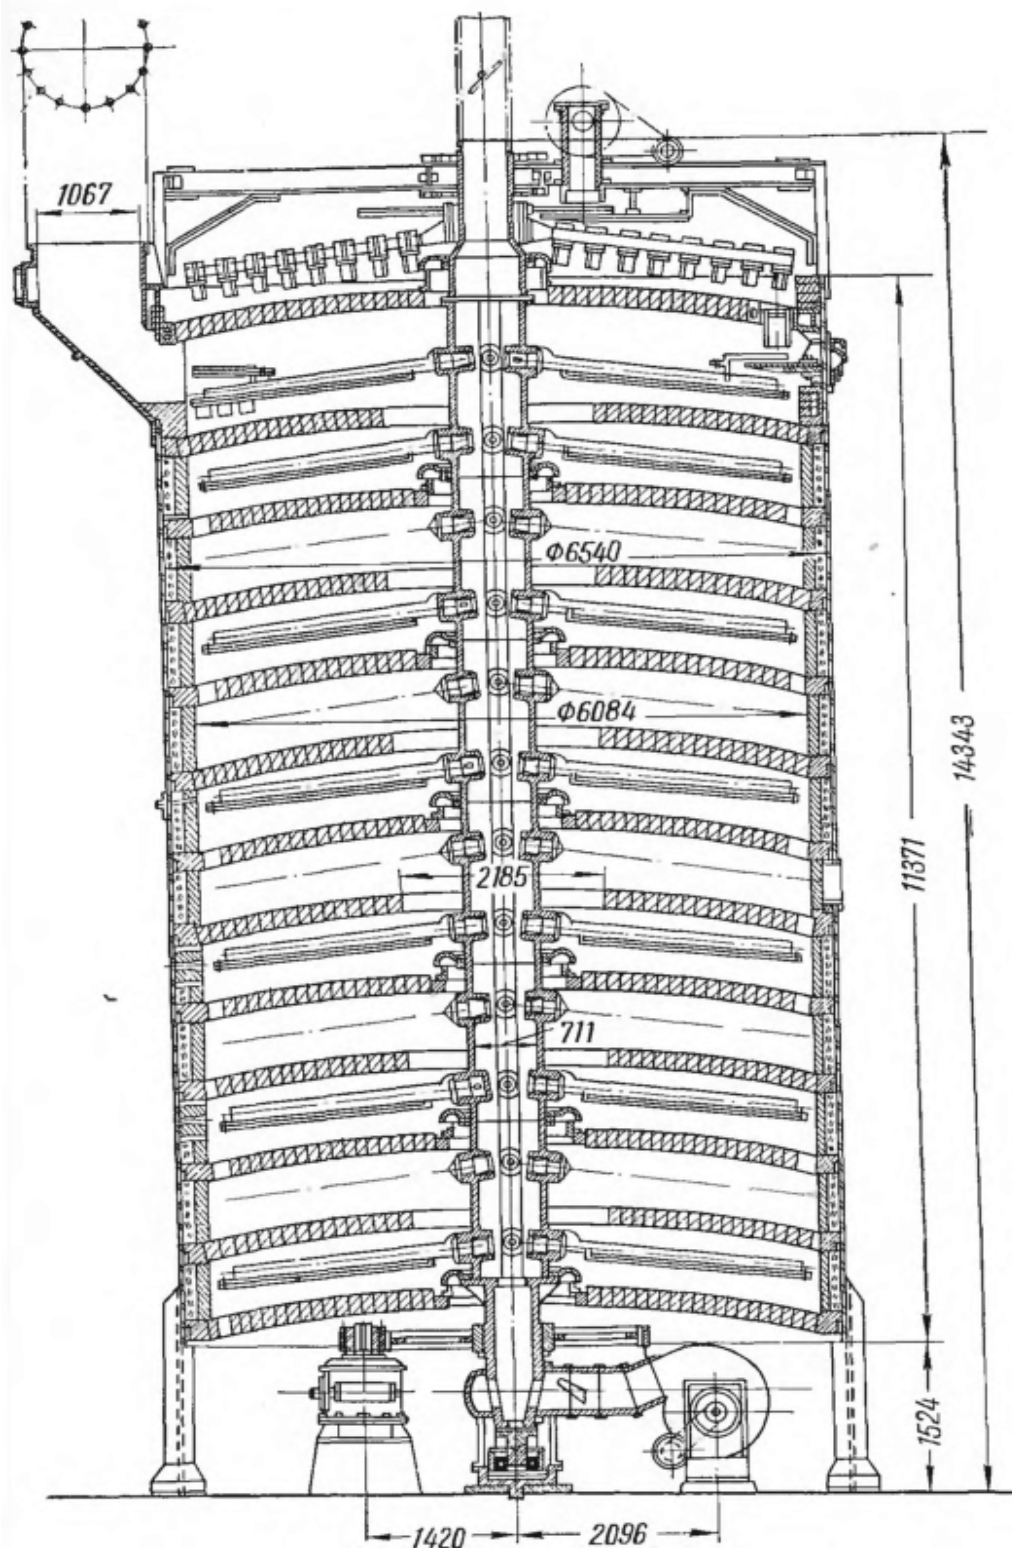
Схема устройства и работы печи для обжига КС
